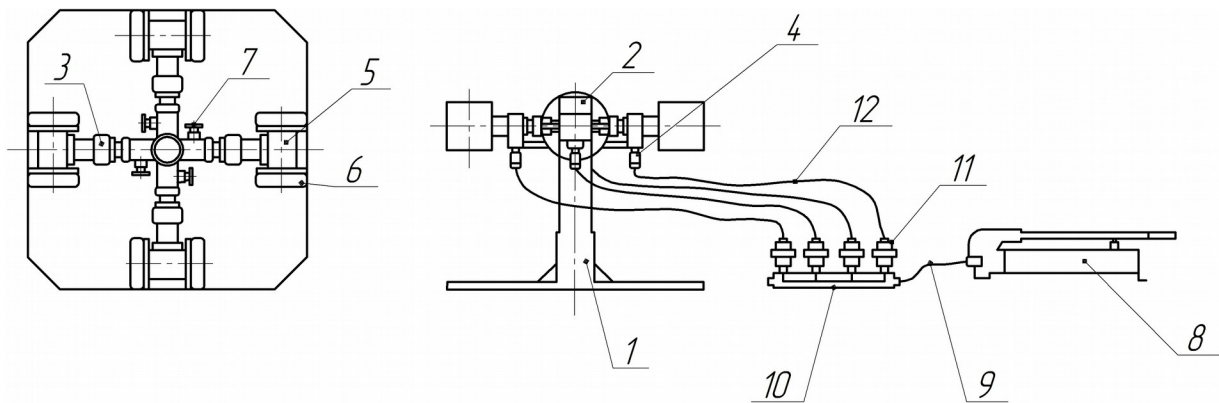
Загальний вигляд установки для ремонту букс УРБ20-4
